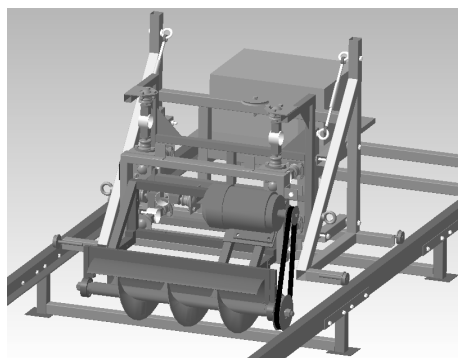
Лабораторный стенд с шнековым рабочим органом
